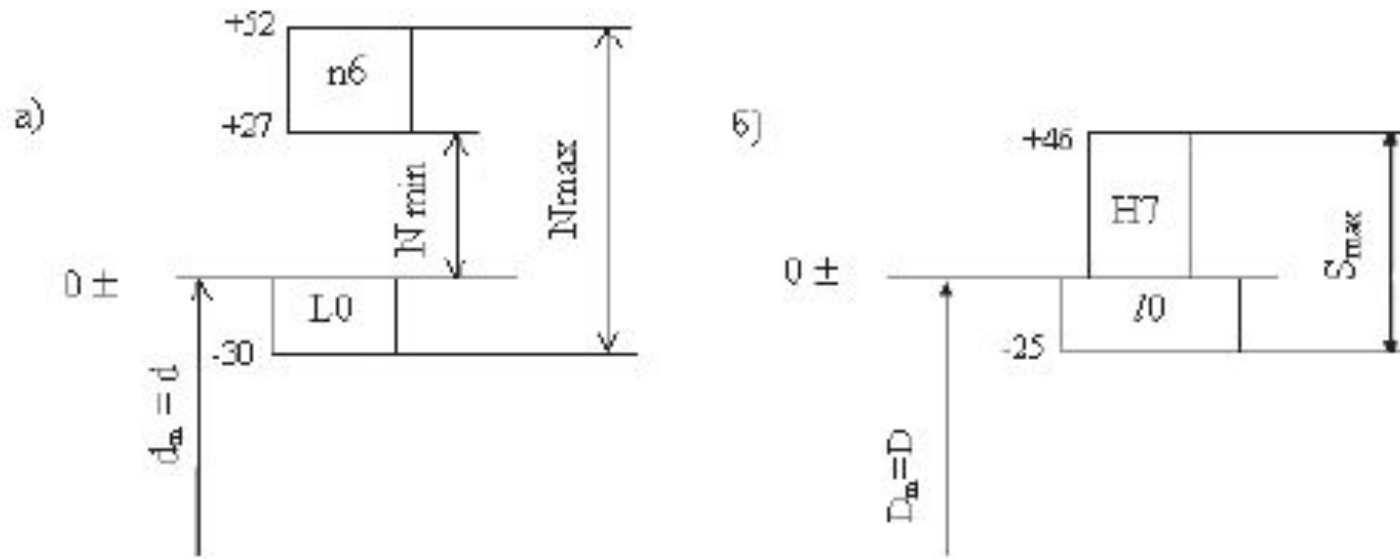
Поля допусков деталей подшипникового соединения:
